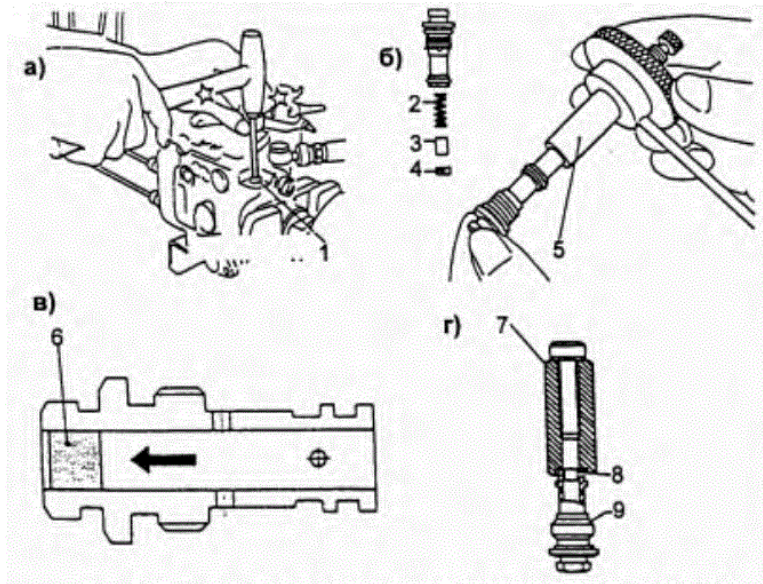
Регулювання редукційного клапана низького тиску
